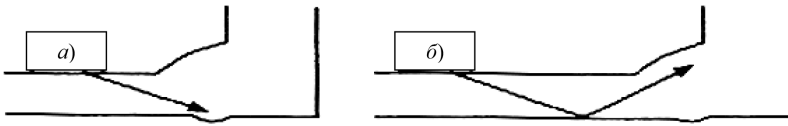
Схемы прозвучивания тавровых сварных соединений со стороны основной детали: а – прямыми лучами преобразователя; б – раздельно-совмещенная схема
